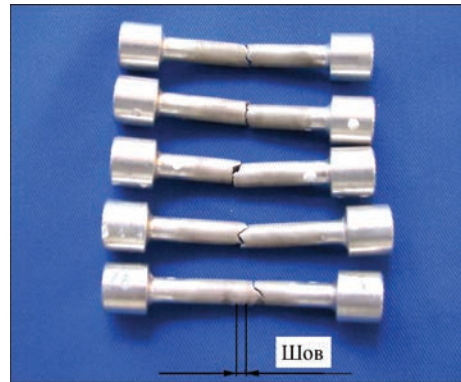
Образцы после механических испытаний на разрыв сварных соединений магниевого сплава МЛ10
